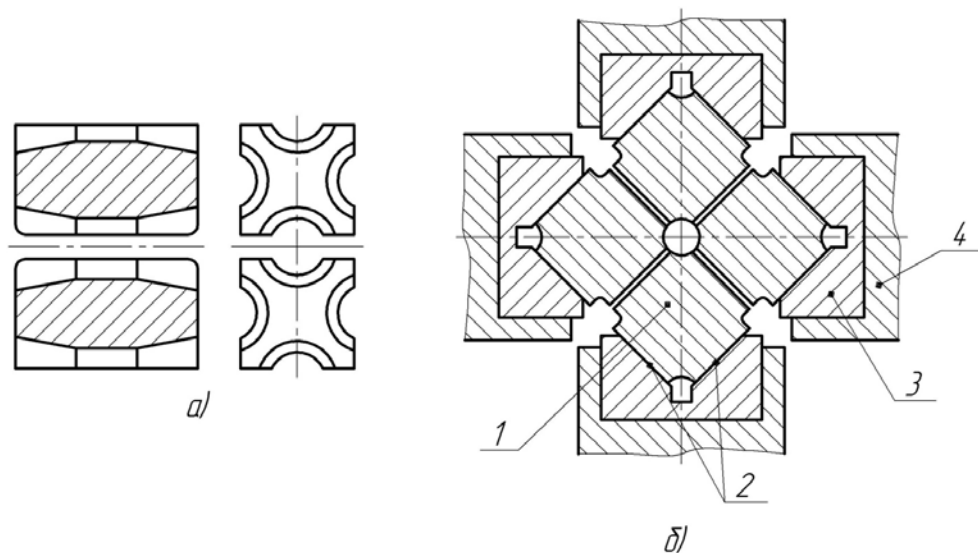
Призматические обжимные бойки: а) базовое исполнение; б) бойки с двумя установочными поверхностями и рабочим профилем в местах пересечения смежных граней [20], 1 – боек; 2 – установочные поверхности; 3 – призма; 4 – подошва ползуна
